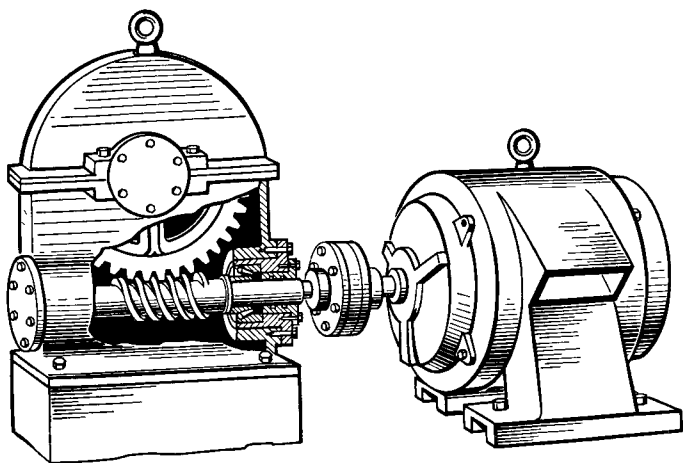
Привод «Электродвигатель — червячный редуктор»
